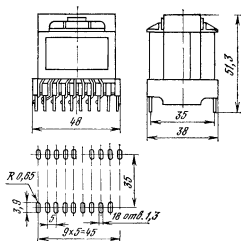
Общий вид, габаритные размеры и разметка печатной платы для установки импульсных трансформаторов питания
